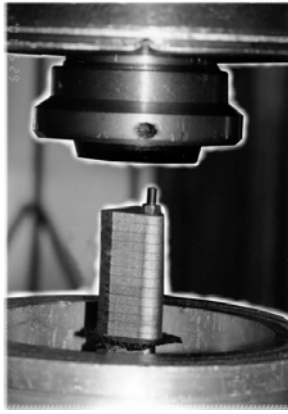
Рабочая зона станка “Дуга-8” при обработке пакета деталей
